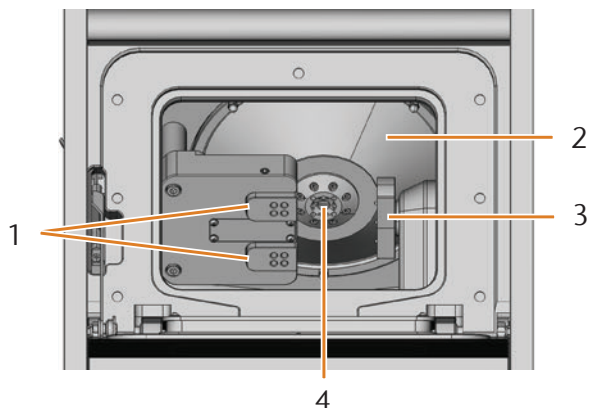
LOCAL DE TRAVAIL DE LA MACHINE N4 IMPRESSION
